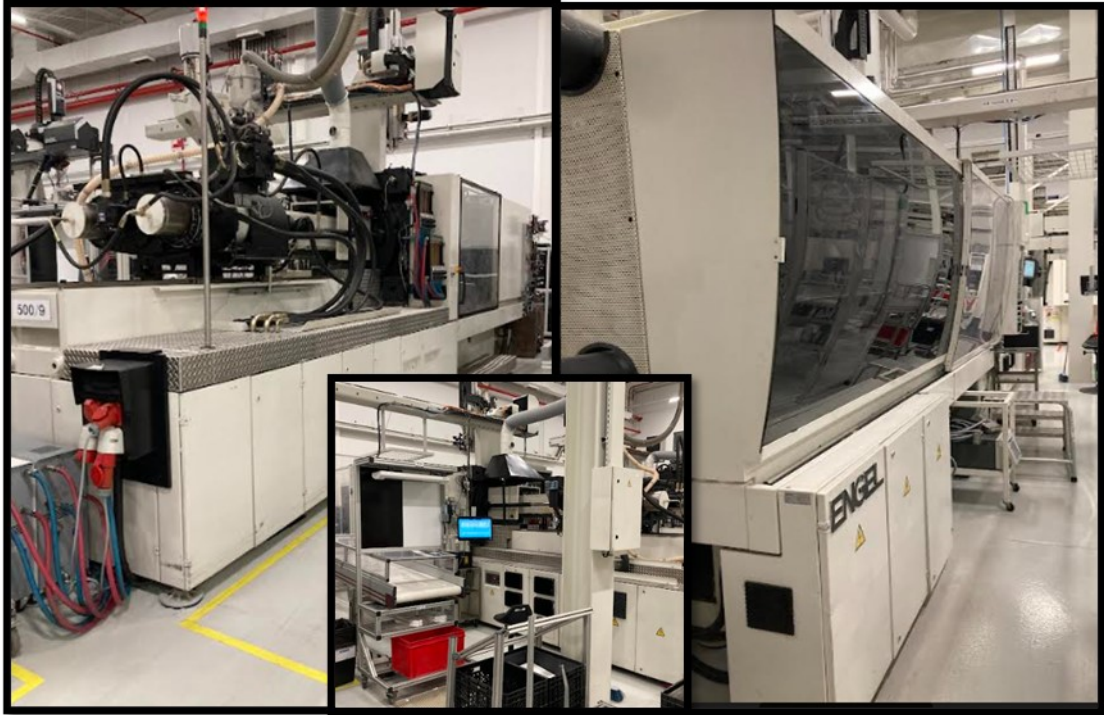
Máquina de moldagem por injeção *Engel CL 2550/500*, de 500 toneladas de força de fecho, utilizada para as produções das peças *Mounting Plate* com o material *Novodur HH-106*.
